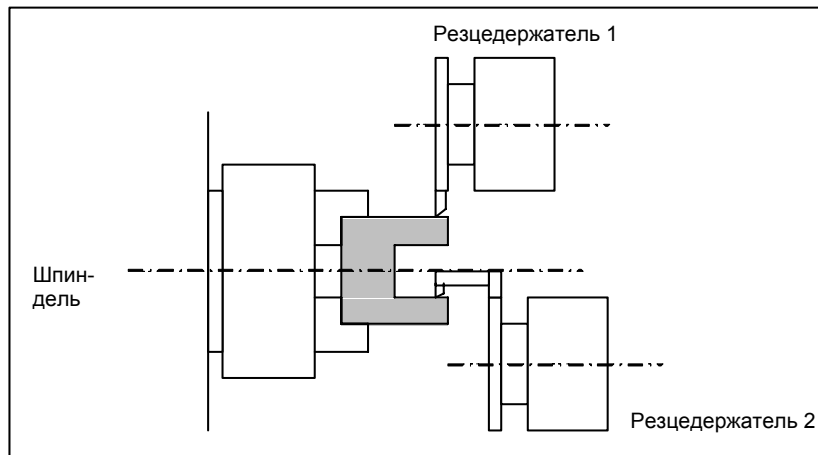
(a) Применение на станке с одним шпинделем и двумя резцедержателями
